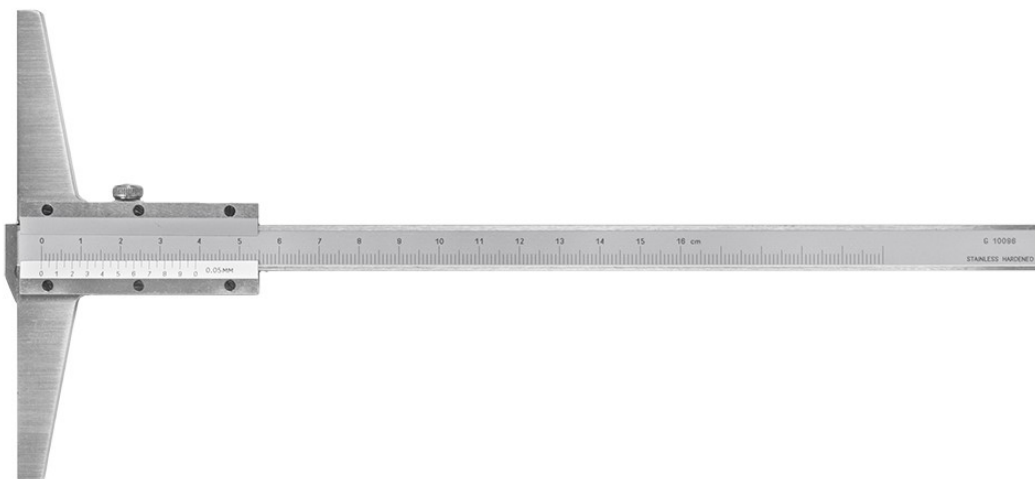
Общий вид штангенглубиномеров ШГ с Г-образной губкой
